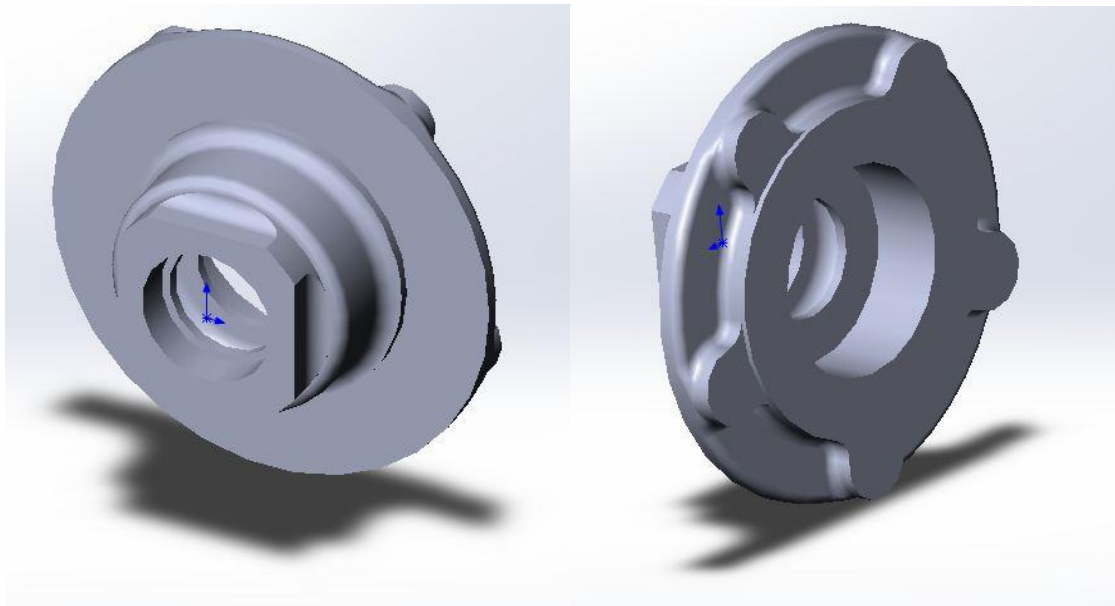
3D-твердотіла модель заготовки «Ступиця»
